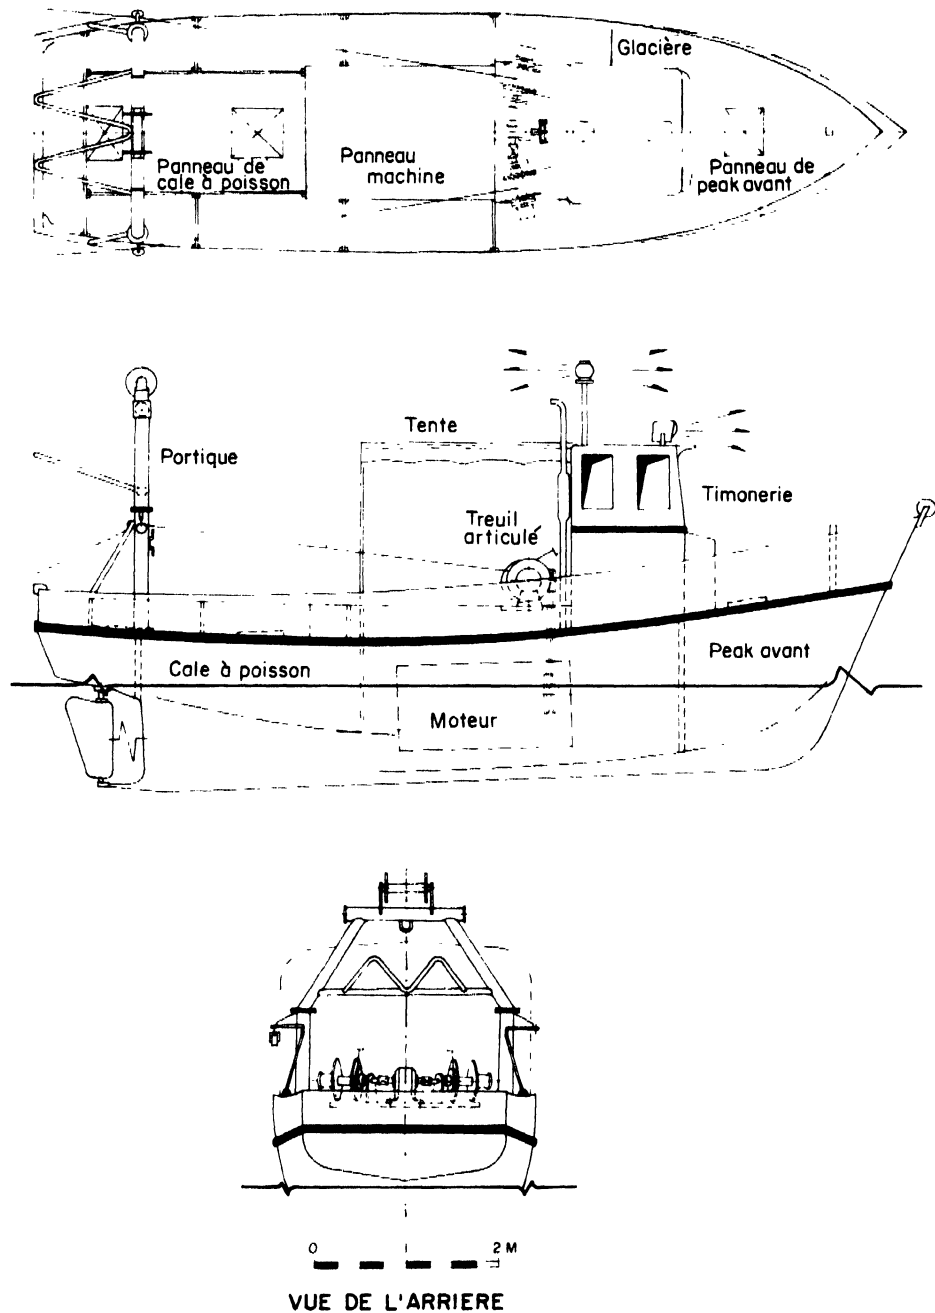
DISPOSITION DE TREUIL A TAMBOUR EN BIAIS ET PORTIQUE SUR PONT DE TRAVAIL
